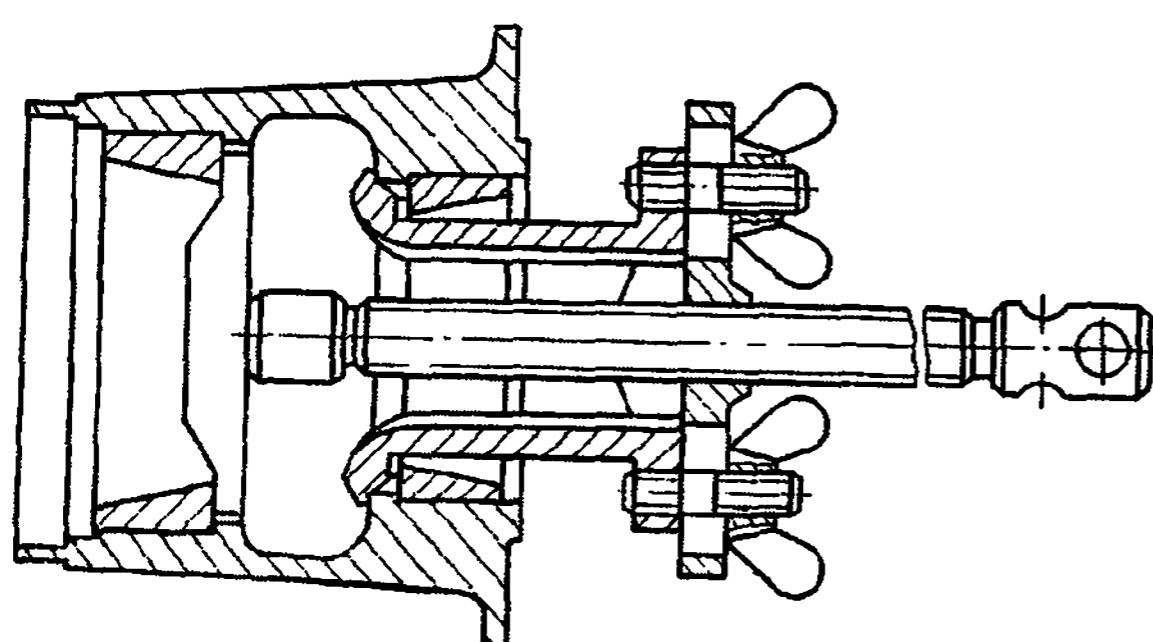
Приспособление для выпрессовки наружных колец подшипников ступиц переднего и заднего колес
